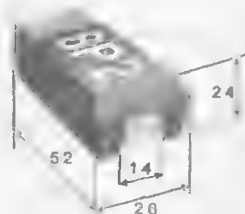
Внешний вид и размеры корпуса DO-214AC
